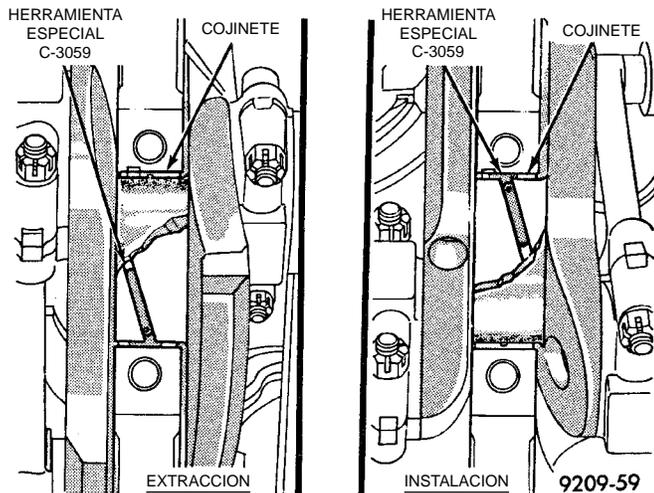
Desmontaje e instalación del cojinete principal superior con la Herramienta C-3059
